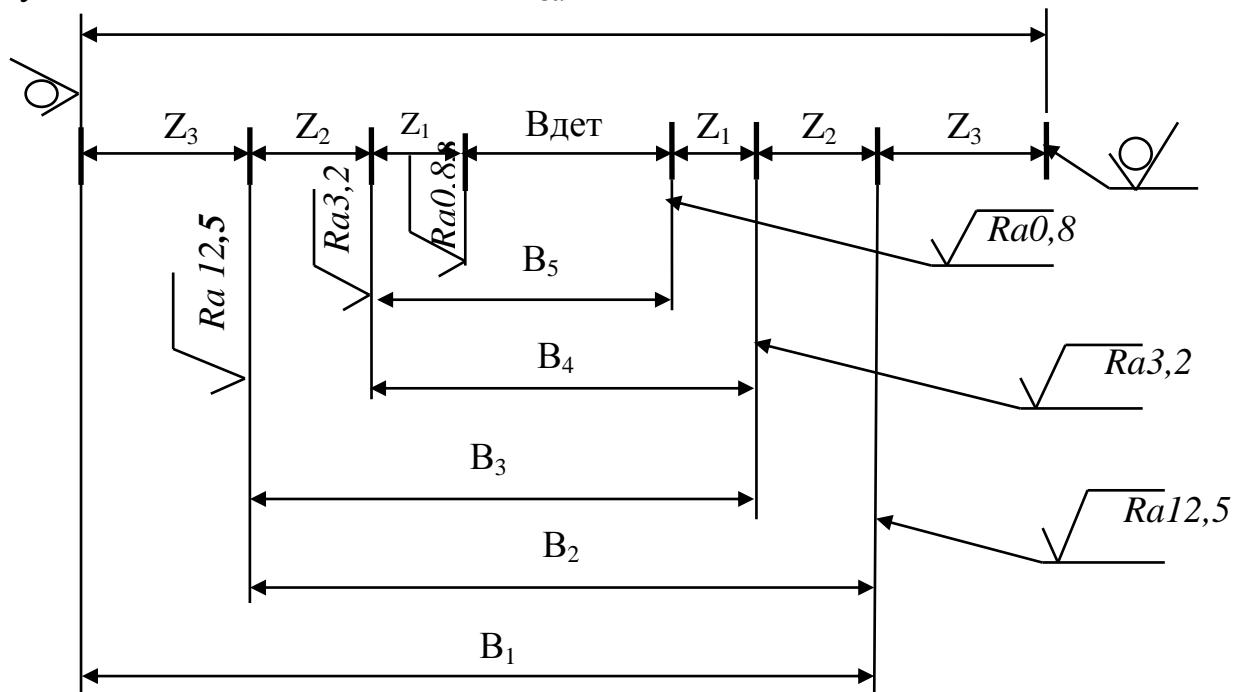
Расчетная схема для вычисления межоперационных размеров при обработке торцевых поверхностей при выполнении черновых и чистовых проходов за одну установку. $B_{\text{дет}}$ – размер готовой детали; $B_{\text{заг}}$ – размер заготовки; Z_1 – припуск на окончательную обработку; Z_2 – припуск на чистовую обработку; Z_3 – припуск на черновую обработку; B_1 – размеры после черновой обработки; B_2 – размеры после чистовой обработки; B_5 – размер после окончательной обработки одного торца
